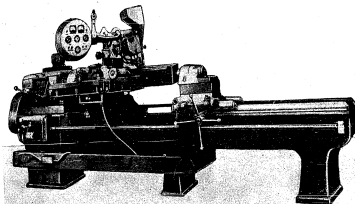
Токарный станок со сварочным аппаратом АДС-1000.
